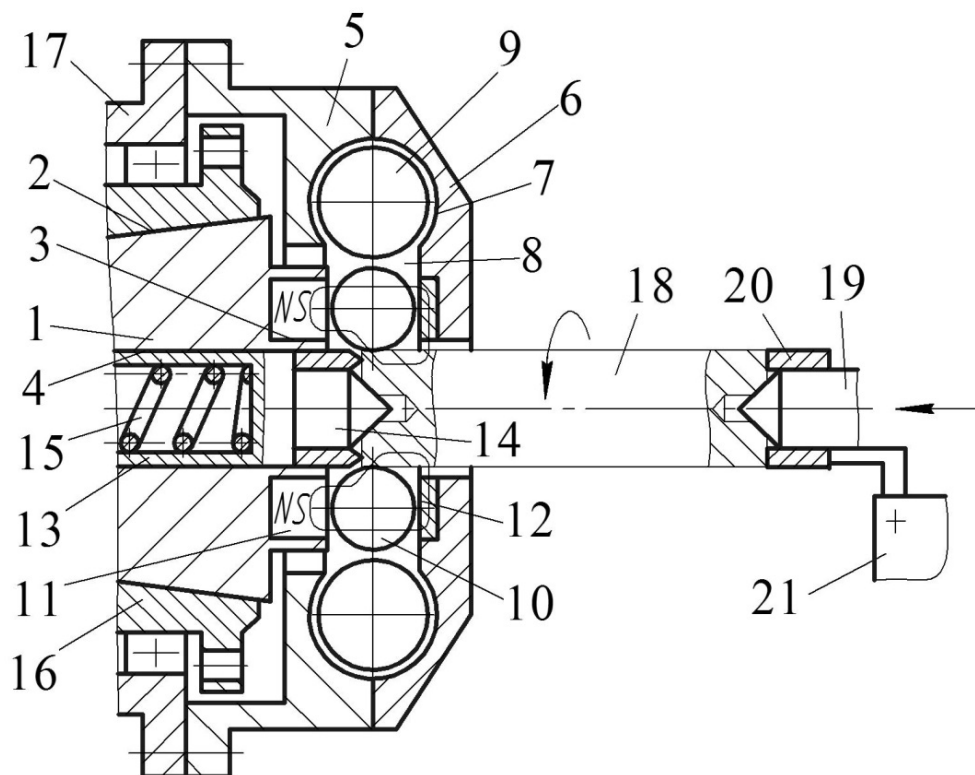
Инструмент для СМДН цилиндрической поверхности валов
